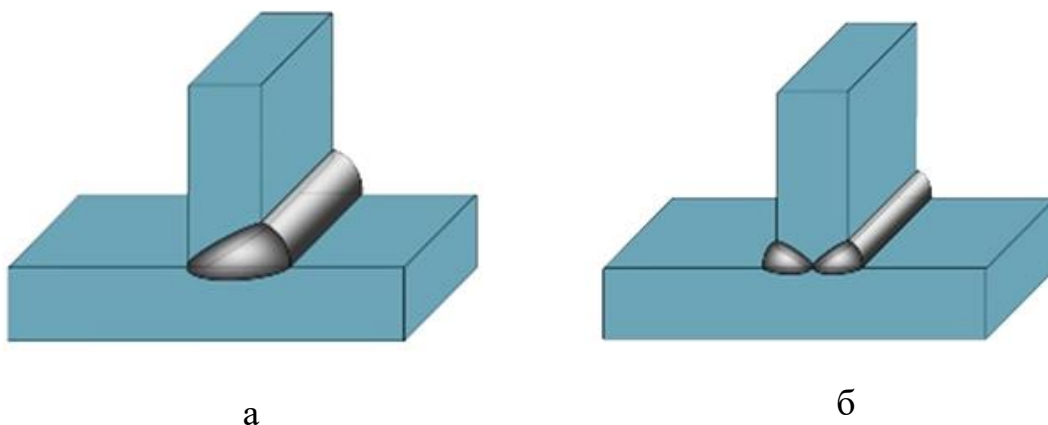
Образец выполнения сварных швов по типу выполнения.
